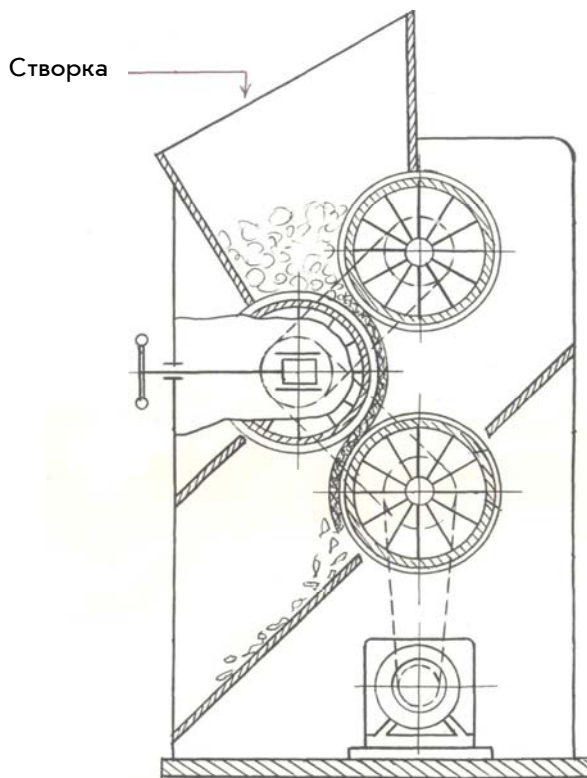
Трехвалковый аппарат для кинематической обработки хлопковой створки
